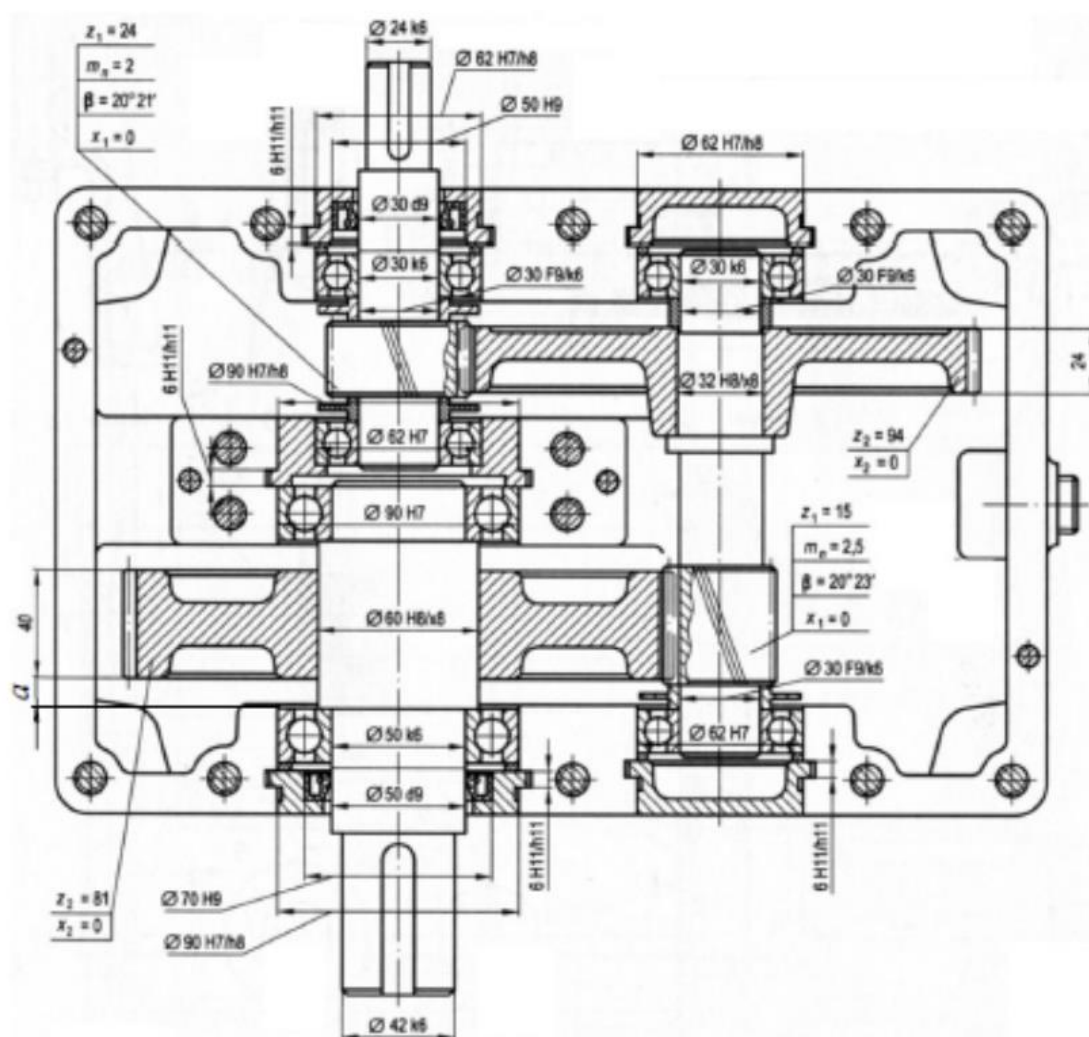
Исполнительный размер a , проставляемый на сборочном чертеже
